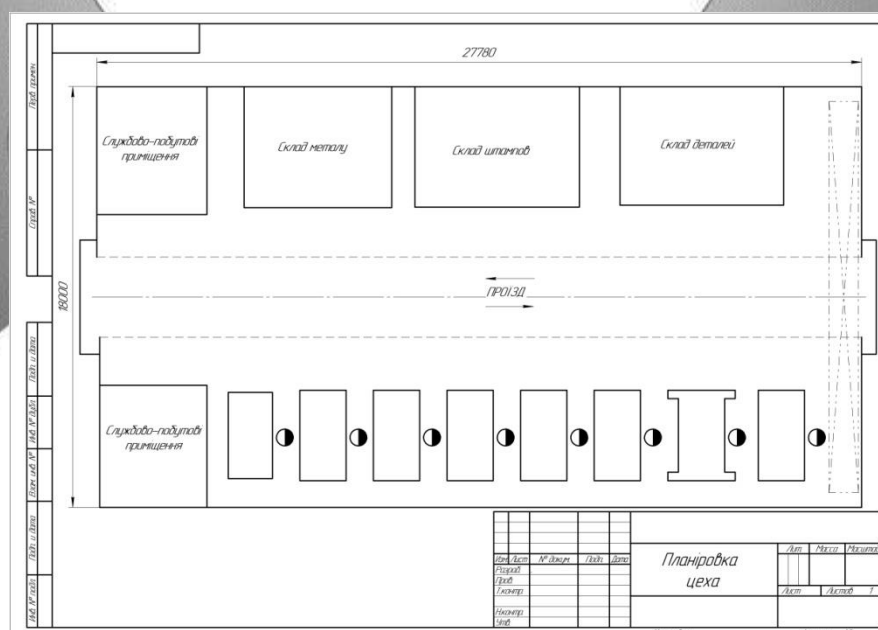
Планіровка цеха, загальний вигляд
